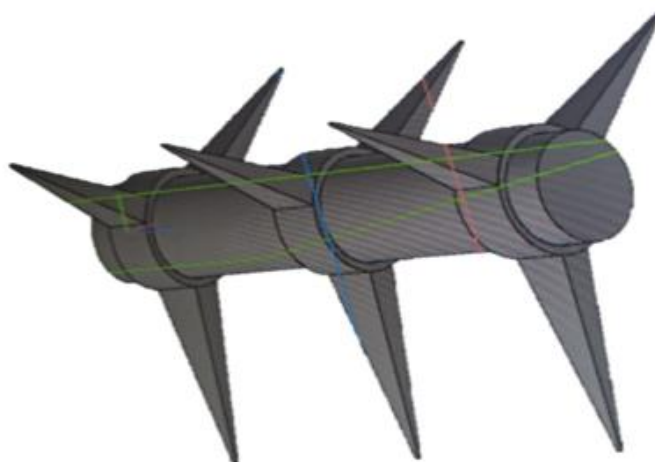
Вал фронтального прокалывателя-щелереза с прокалывающими элементами
